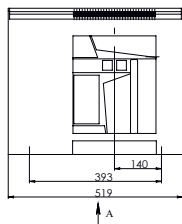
Габаритные размеры выдвижных четырехполюсных выключателей типоразмера F
